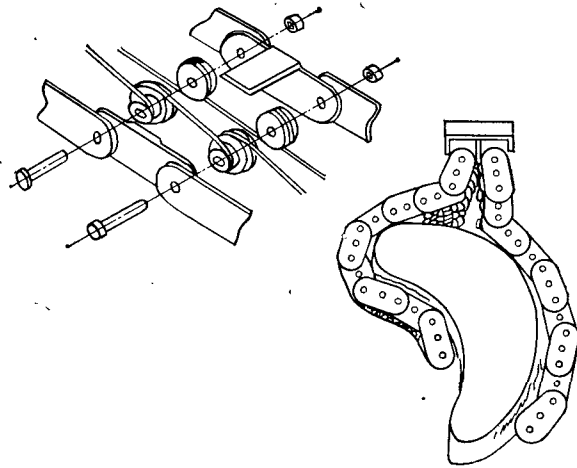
Конструкция схвата, подстраивающегося под форму захватываемого предмета. (По данным *Revue Microtechnique*.)
